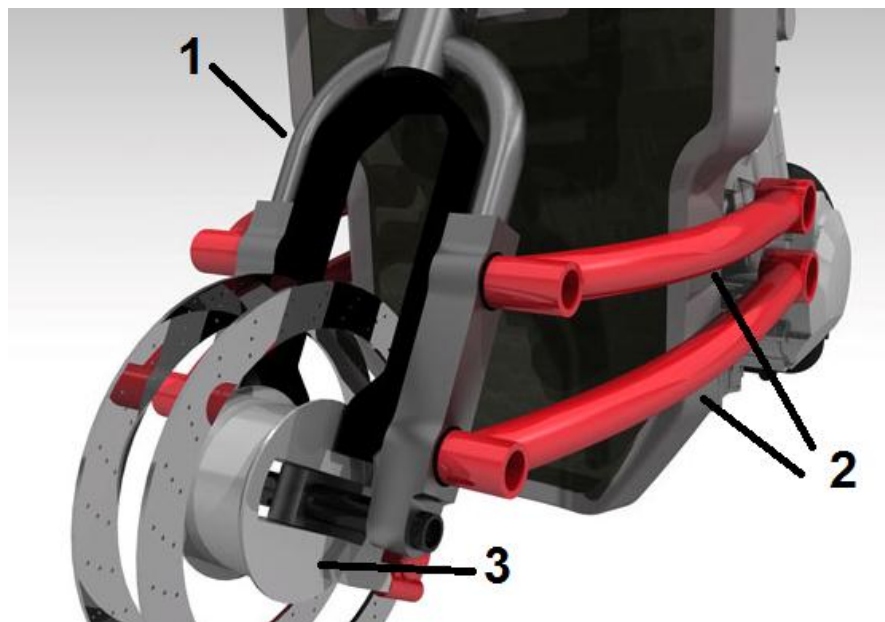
Primer esquema de la suspensión delantera de LaMoto2. 1) Horquilla de suspensión. 2) Basculantes superpuestos. 3) Bujes.
